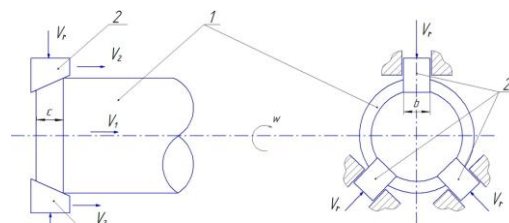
Принципиальная схема формирования усеченного конуса на заднем конце цилиндрической заготовки с помощью инструмента деформации в процессе обжатия в трехвалковом стане радиально-сдвиговой прокатки
